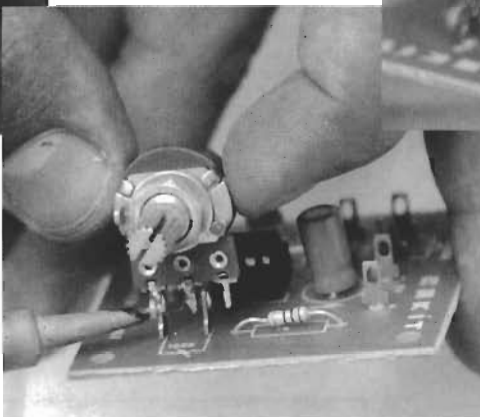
Para el ensamblaje de la tarjeta del relé solamente se requiere poner atención al plano esquemático y a las indicaciones que están en el circuito impreso.
